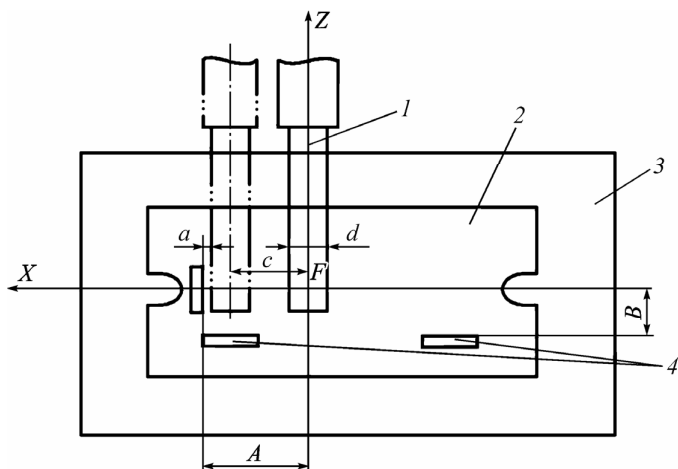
Схема выверки приспособления на поворотном столе станка по оси шпинделя с помощью мерной оправки:
